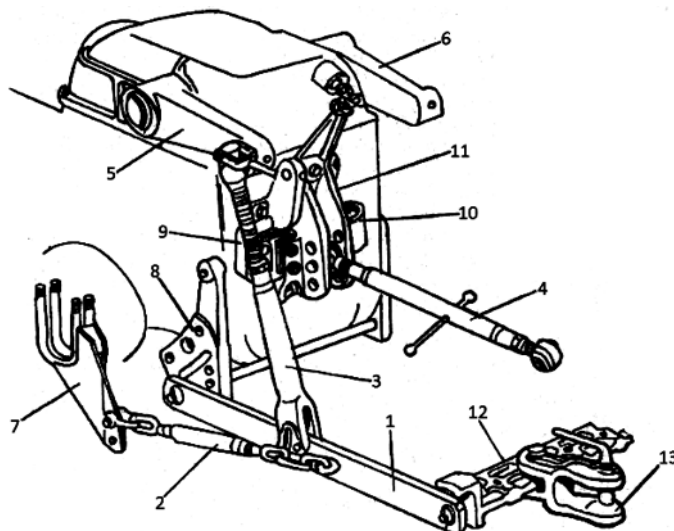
Mecanismul de suspendare al tractorului cu instalație hidraulică monobloc:
